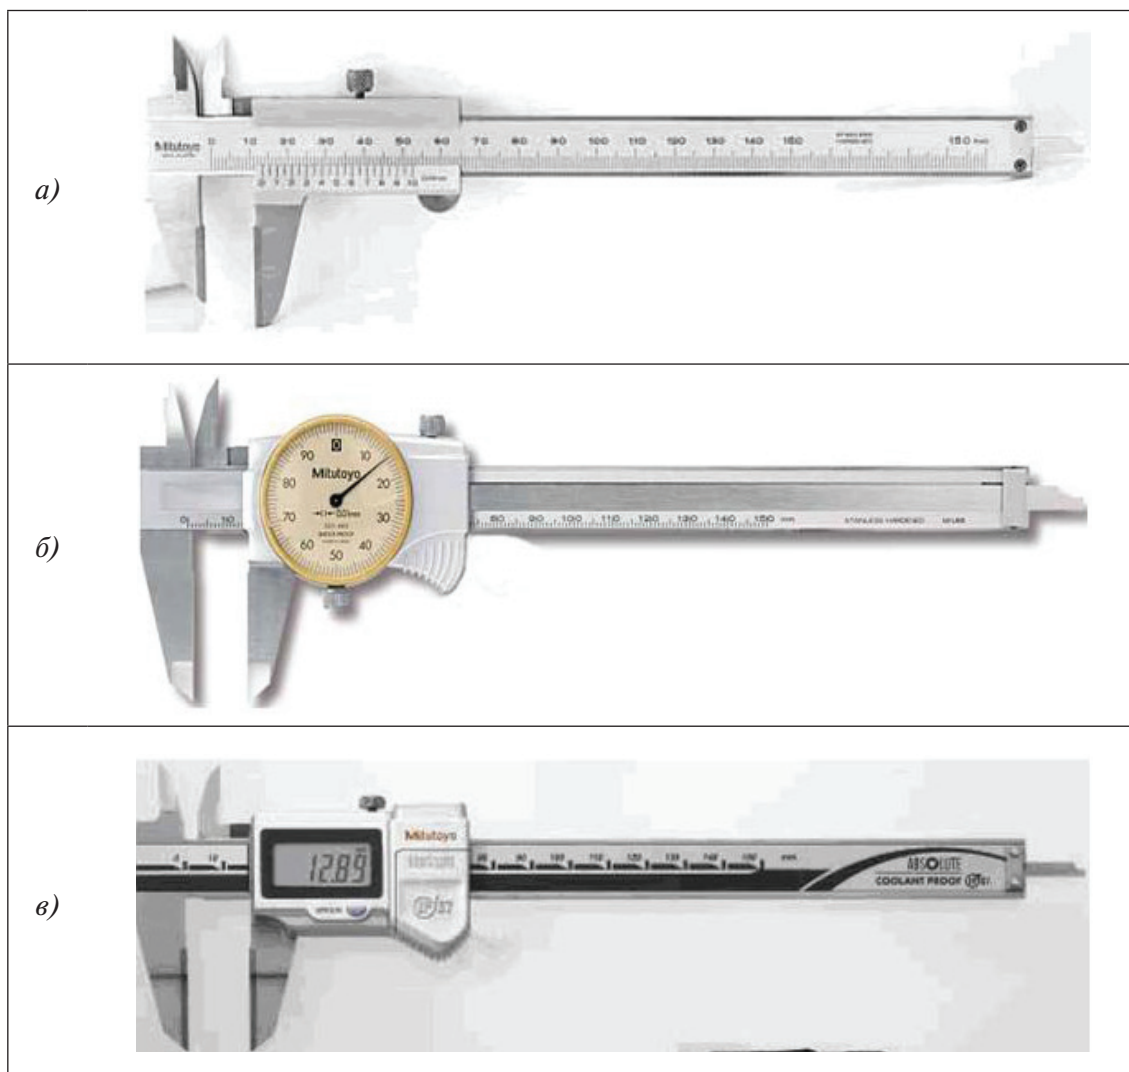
Штангенциркули. *a* – разметочный с глубиномером; *б* – с круговой шкалой; *в* – для измерений узких пазов
